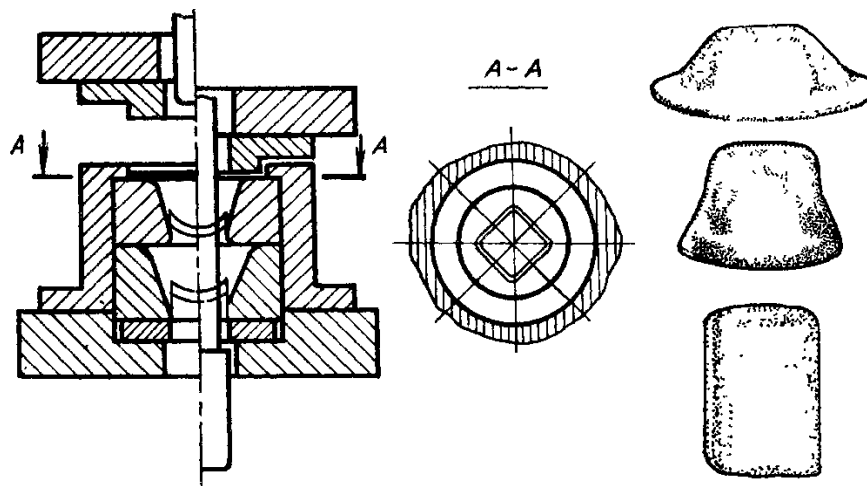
Схема штампа с комбинированной матрицей для, вытяжки высокой квадратной коробчатой детали
